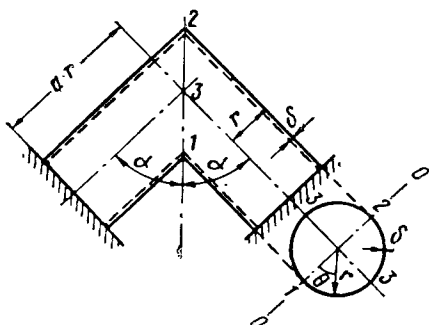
Расчетная схема пересечения двух трубопроводов под произвольным углом (без усиления по линии пересечения)
